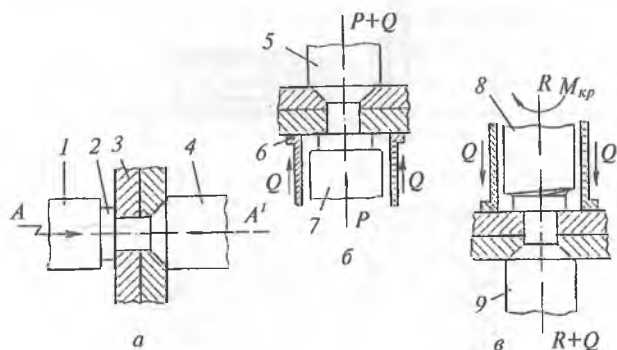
Образование замыкающих головок заклепок: а — ударом; б — прессованием; в — раскатыванием; 1 — обжимка молотка; 2 — замыкающая головка; 3 — соединяемые детали; 4 — поддержка; 5 — верхний пуансон; 6 — прижим; 7 — нижний пуансон; 8 — раскатник; 9 — опорный пуансон
